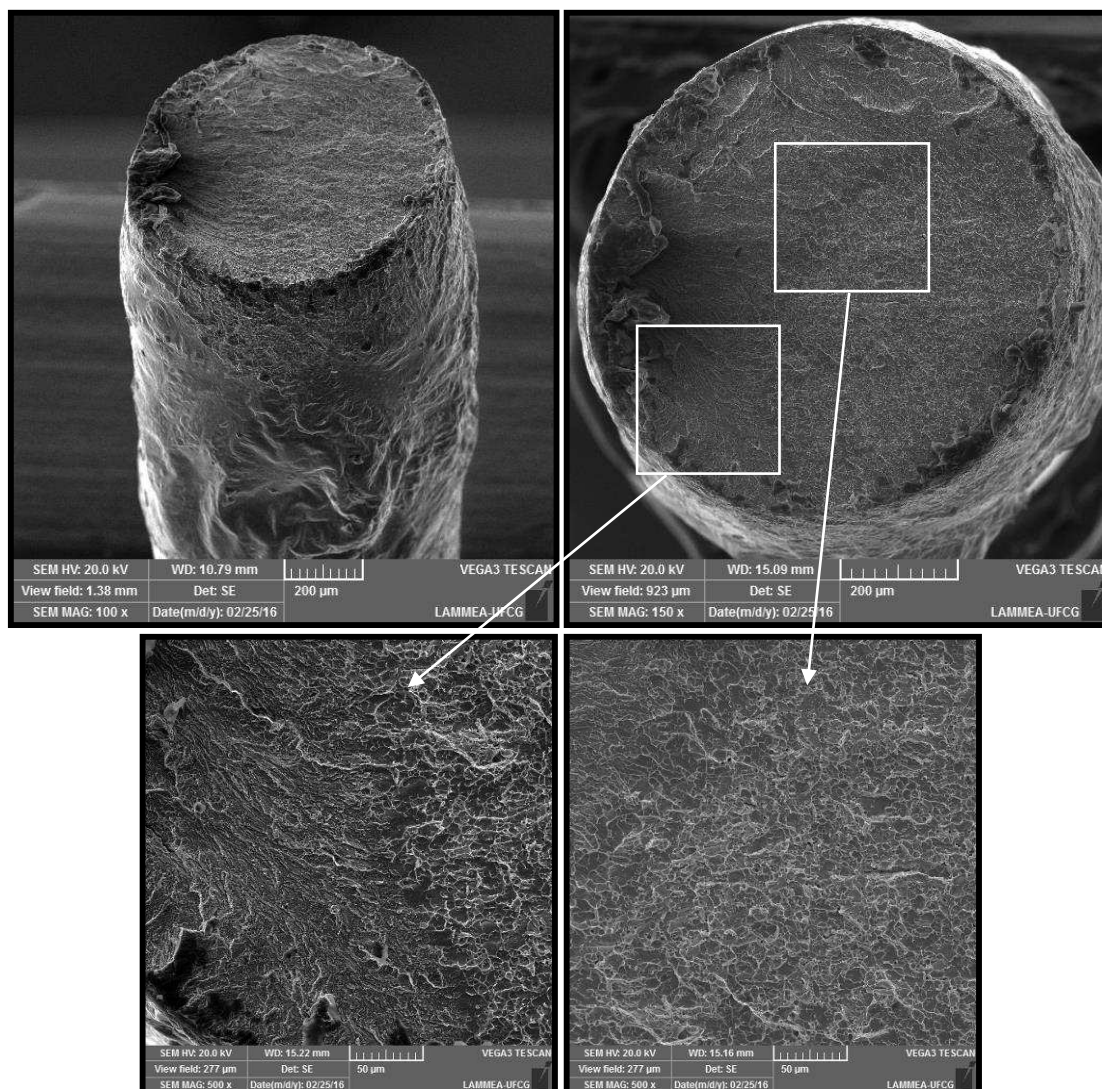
Superfície de fratura do fio superelástico soldado na configuração 9ms/60% e testado a 90°C.
